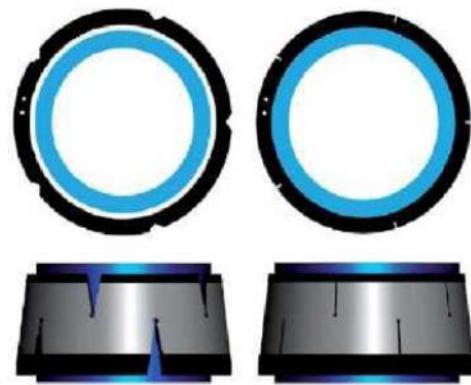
Принцип работы конической сварочной манжеты: разрывы обеспечивают возможность эластичного уменьшения диаметра при заполнении манжетой зазора между трубой и муфтой
